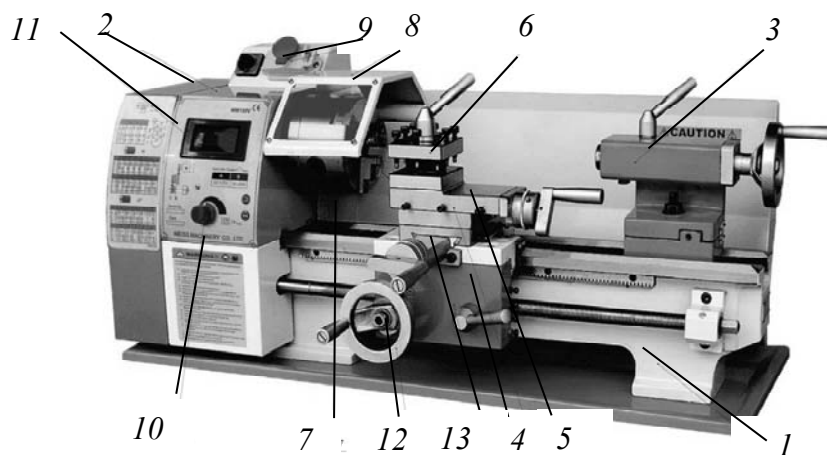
Общий вид токарного настольного станка Universal WM180V
